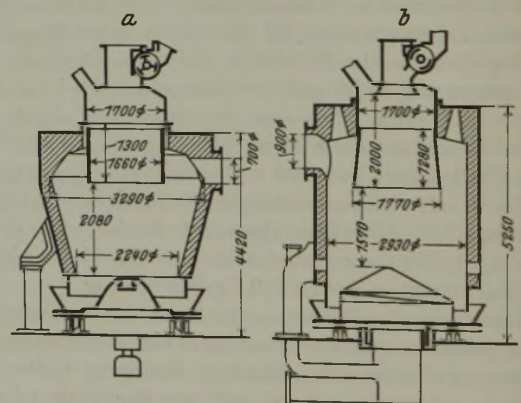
Gaserzeuger mit Schwelteinbau und selbsttätiger Beschickung.
